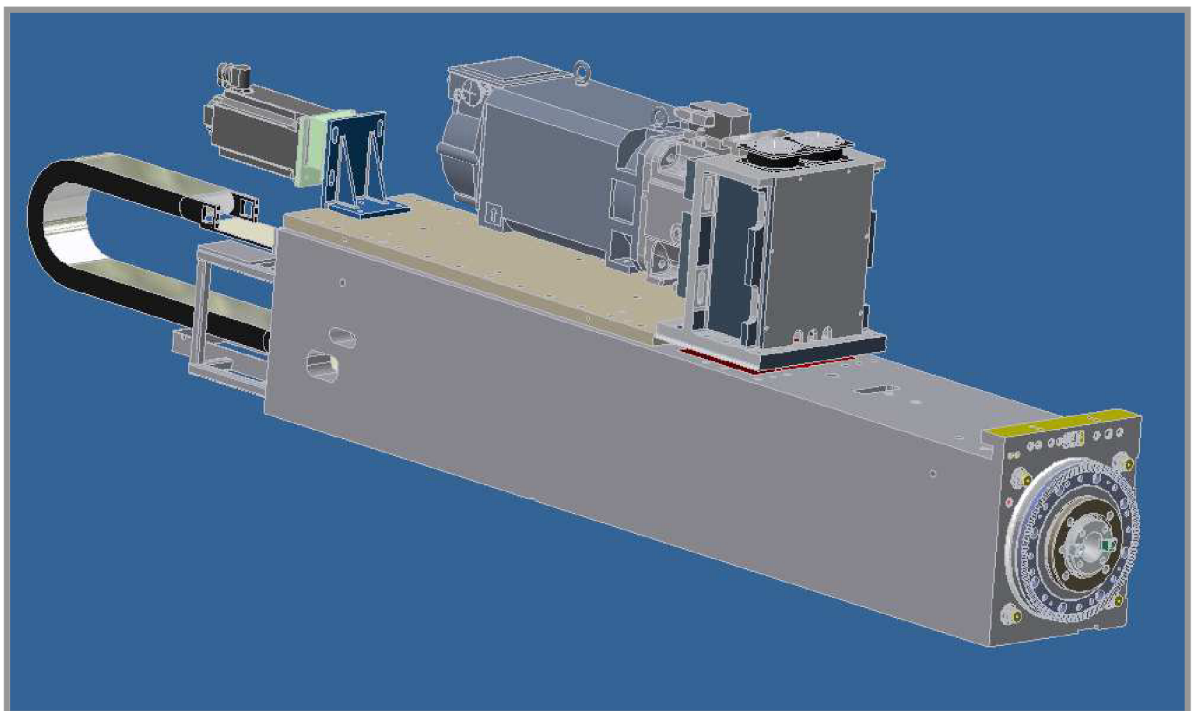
Univerzální frézovací hlava firmy Cyttec [5]
